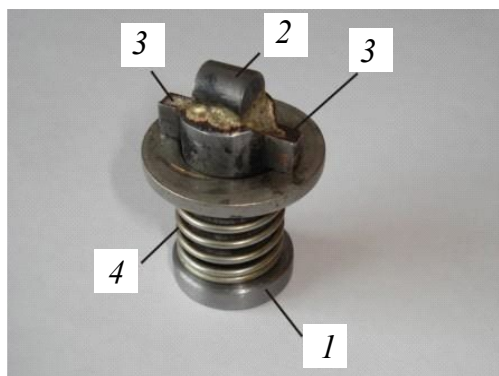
Корпус для крепления индентора с установленной в него вставкой, разработанный для устройства «Прочностномер ПСШ-1»
